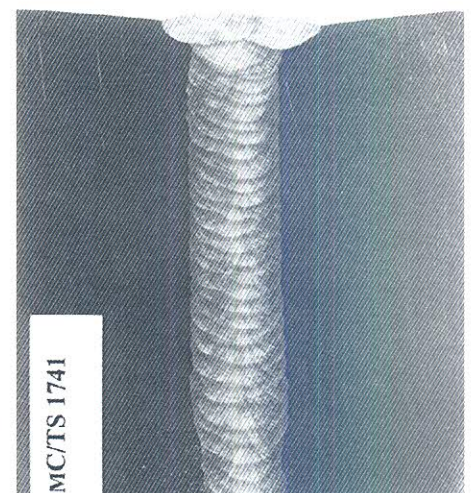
Фотография шлифа шва открытого для всех участников образца после сварки и до зачистки поверхности (по данным TRUEFLAW). Показана форма разделки шва и структура многопроходного заполнения шва
